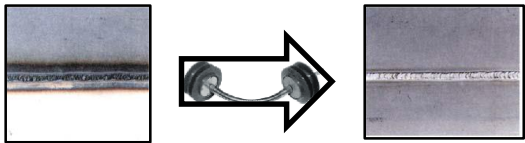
Soldadura a Tope Tubo a Tubo [4].
